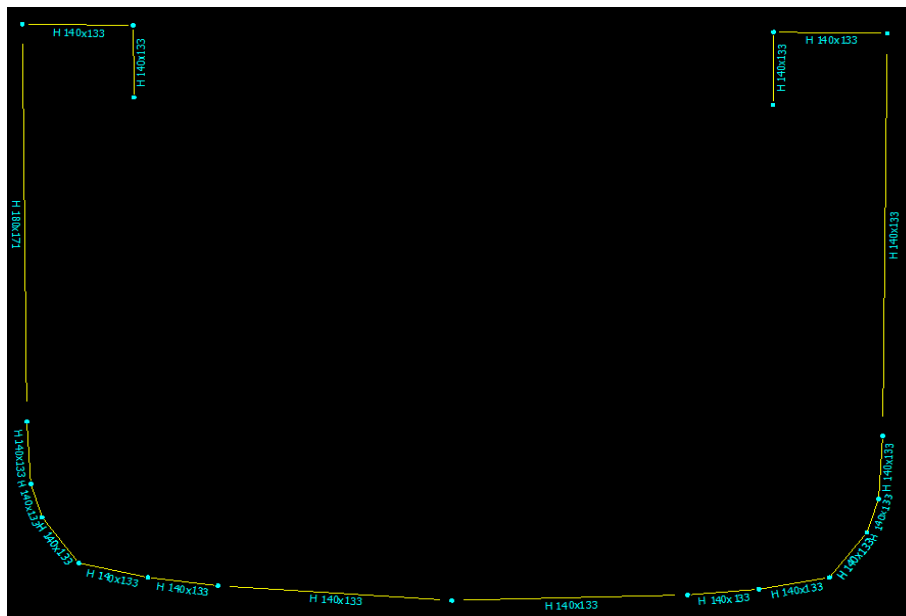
Reforzamiento transversal de la parte interior de la estructura de protección.
